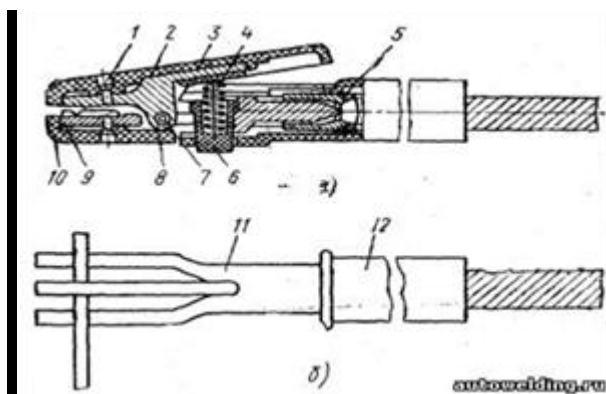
Электрододержатели для ручной дуговой сварки
